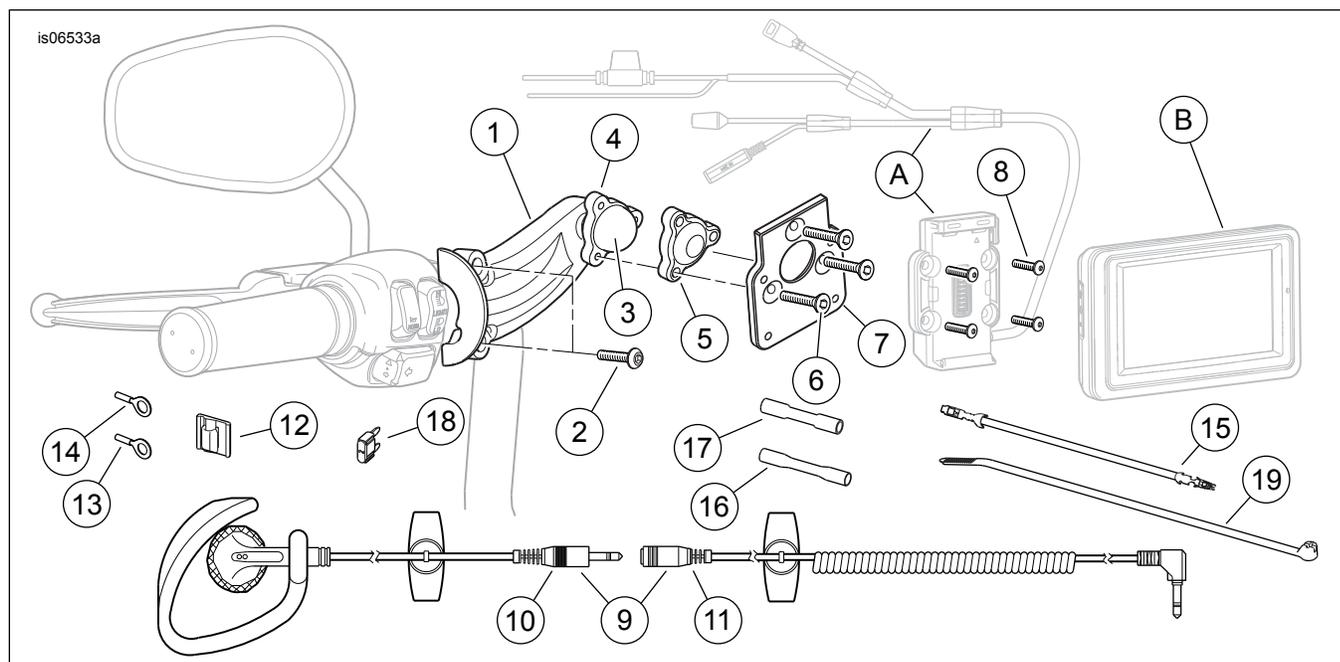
Pièces de rechange, kit de montage sur guidon de GPS Road Tech Zumo 660 et Zumo 665
